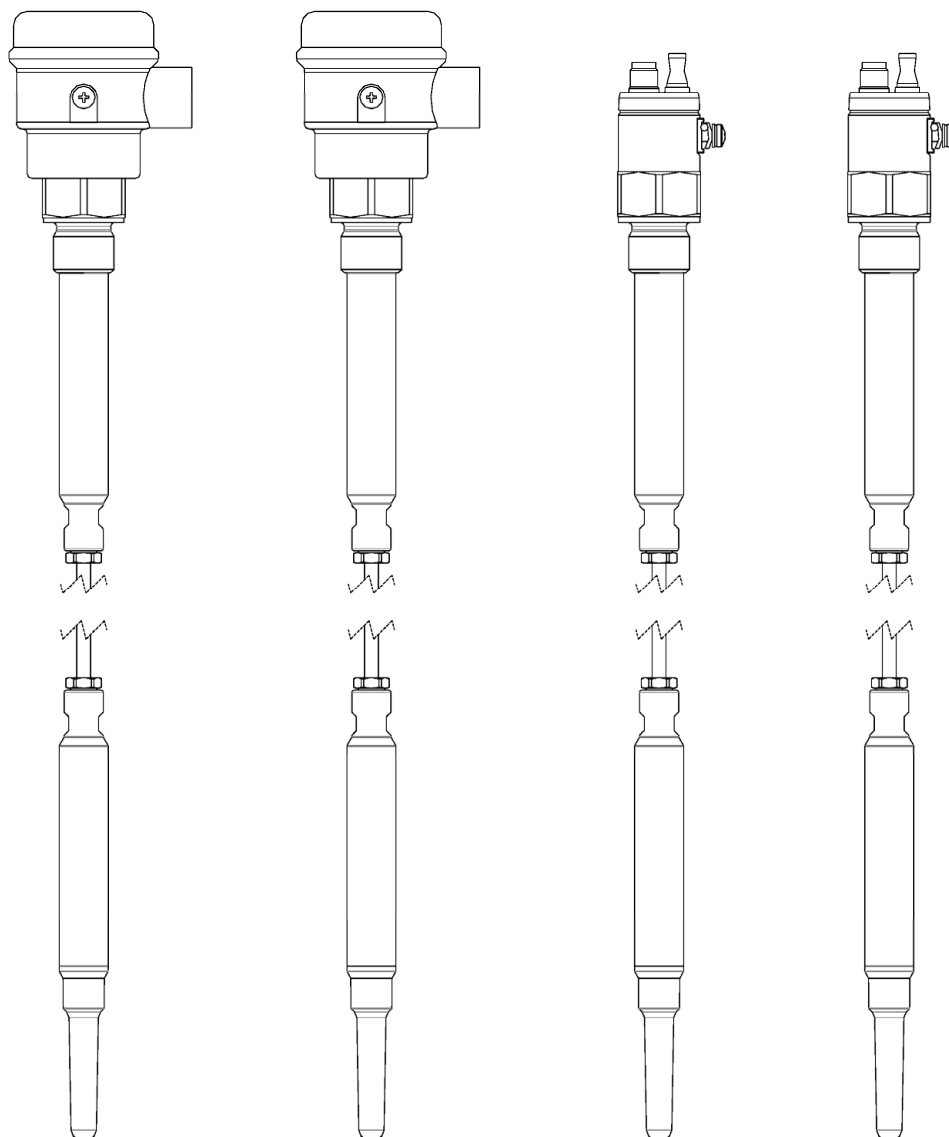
Version mit Kabelverlängerung Typ CN 7150
